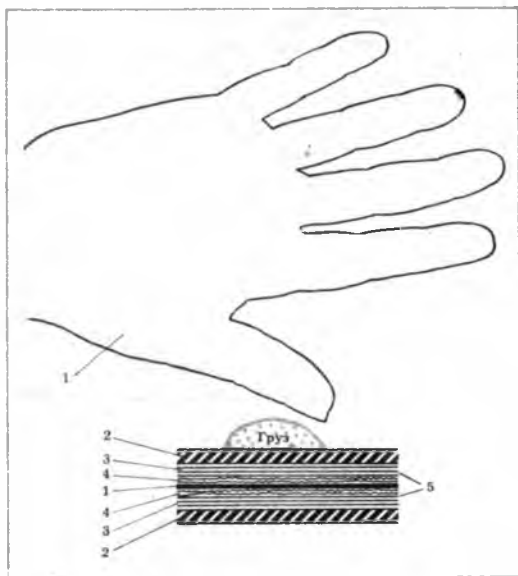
Изготовление полиэтиленовых перчаток: 1 — перчатки из нихромовой проволоки; 2 — лист резины; 3 — газета (2 слоя); 4 — полиэтилен (2 слоя); 5 — калька
